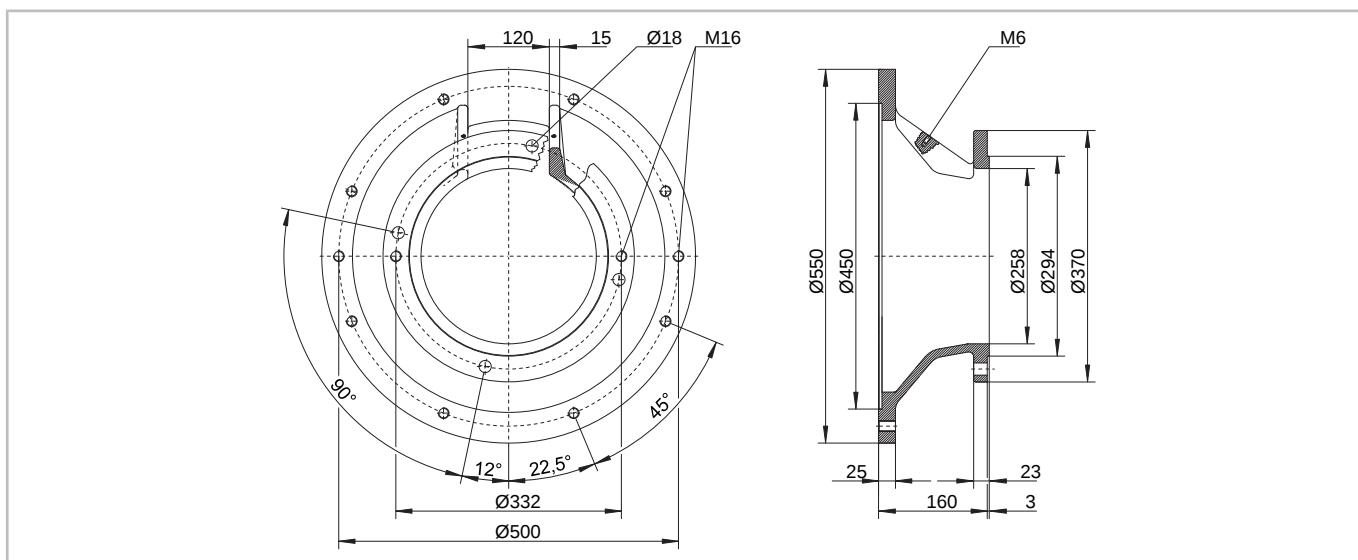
Габаритный чертеж кожуха муфты GS7120
